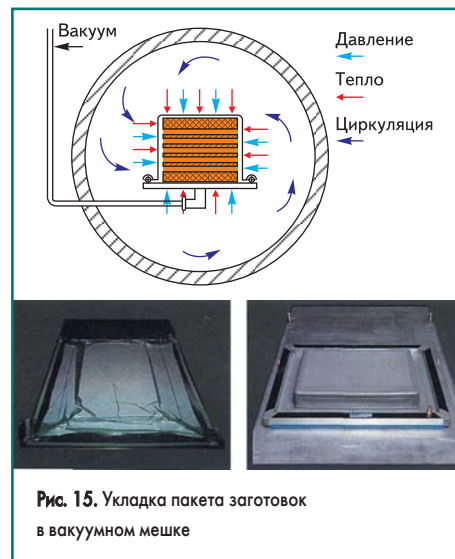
Укладка пакета заготовок в вакуумном мешке
